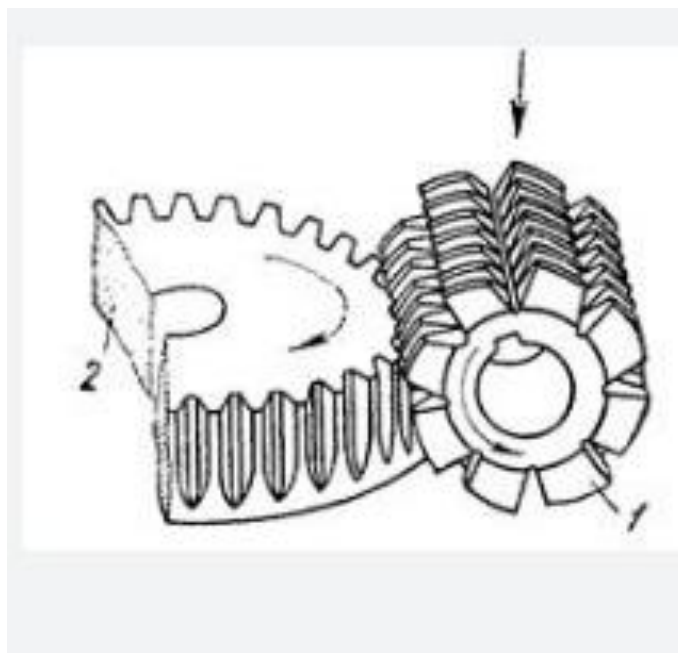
Обработка зубчатых колес червячными фрезами
